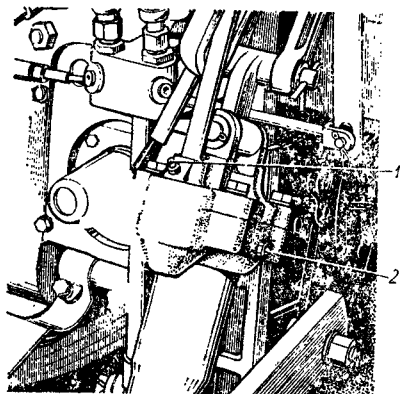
Смазывание подшипников и редуктора правого раскоса
